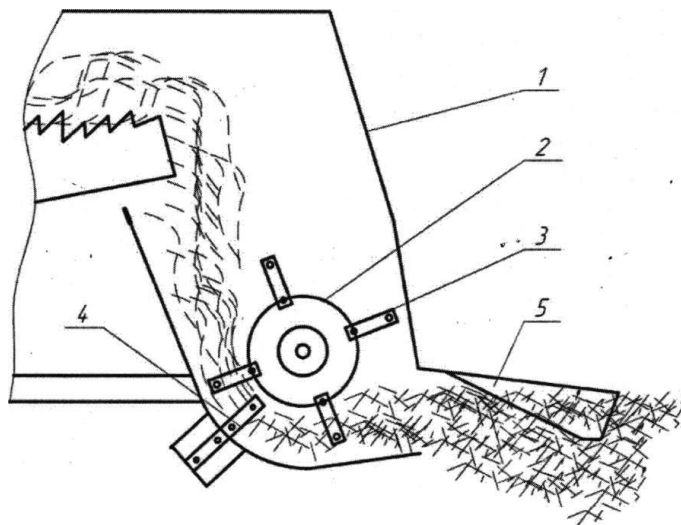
Технологическая схема измельчителя соломы зерноуборочного комбайна: 1 - корпус измельчителя; 2 - измельчающий барабан; 3 - нож измельчающего барабана; 4 - противорежущее устройство; 5 - разбрасыватель
